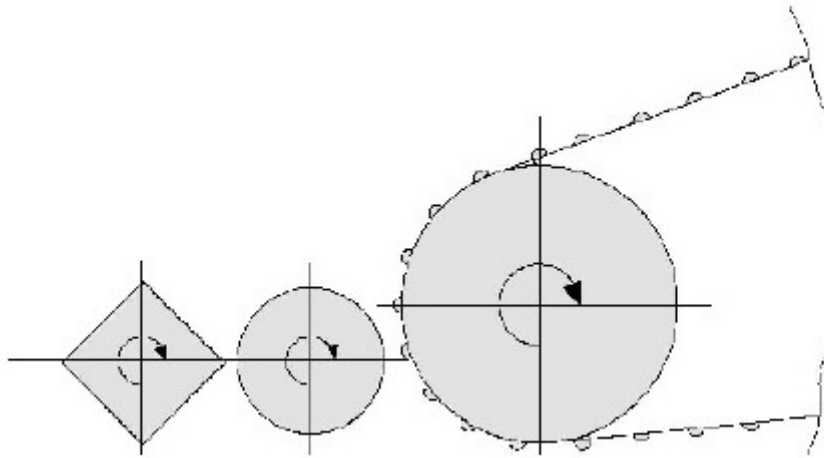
Схема валикового робочого органу, що підкопує.
